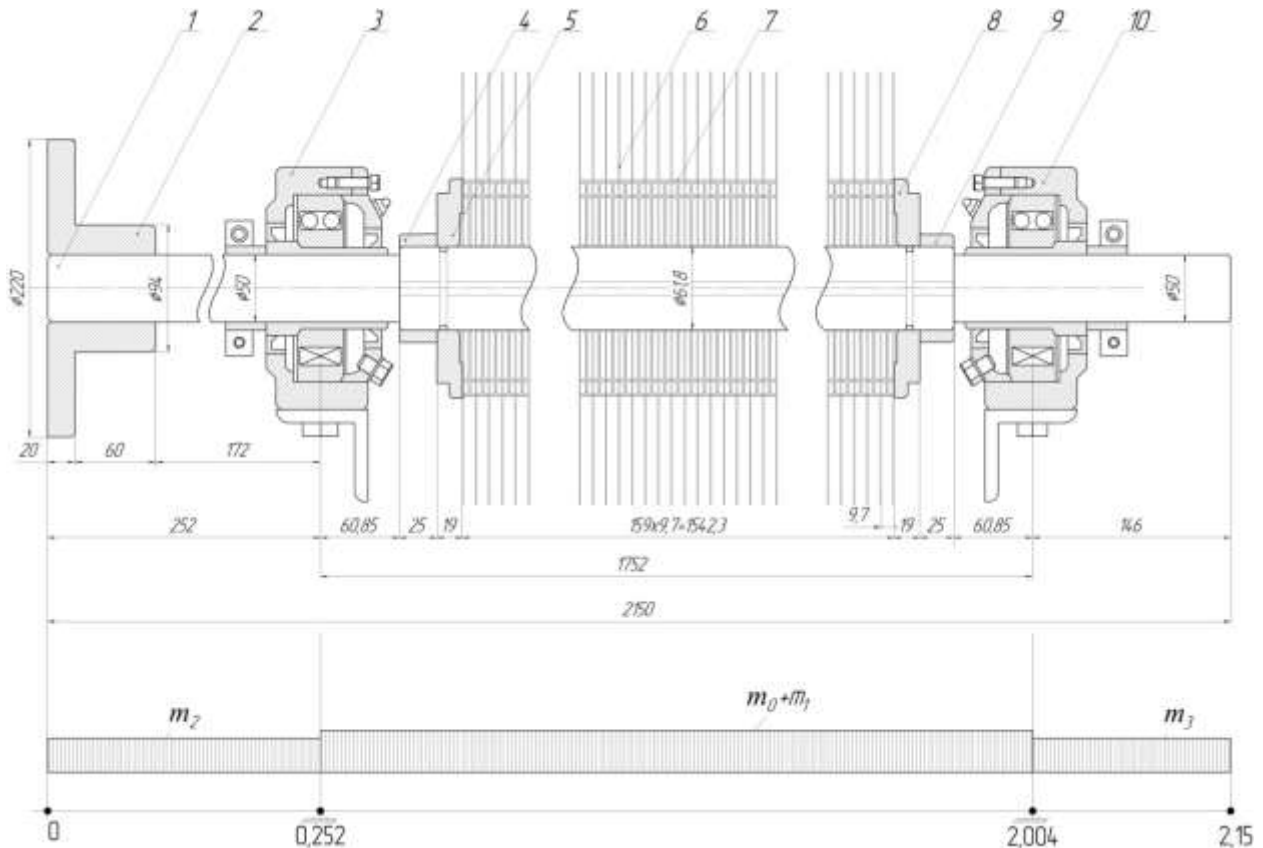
Расчетная схема пильного цилиндра линтерной машины. 1 – Вал , 2 – Полумуфта; 3, 10 – Корпус подшипников; 4, 9 – Гайки; 5, 8 – Шайбы; 6 – Пильные диски, 7 – Междупильные прокладки.
